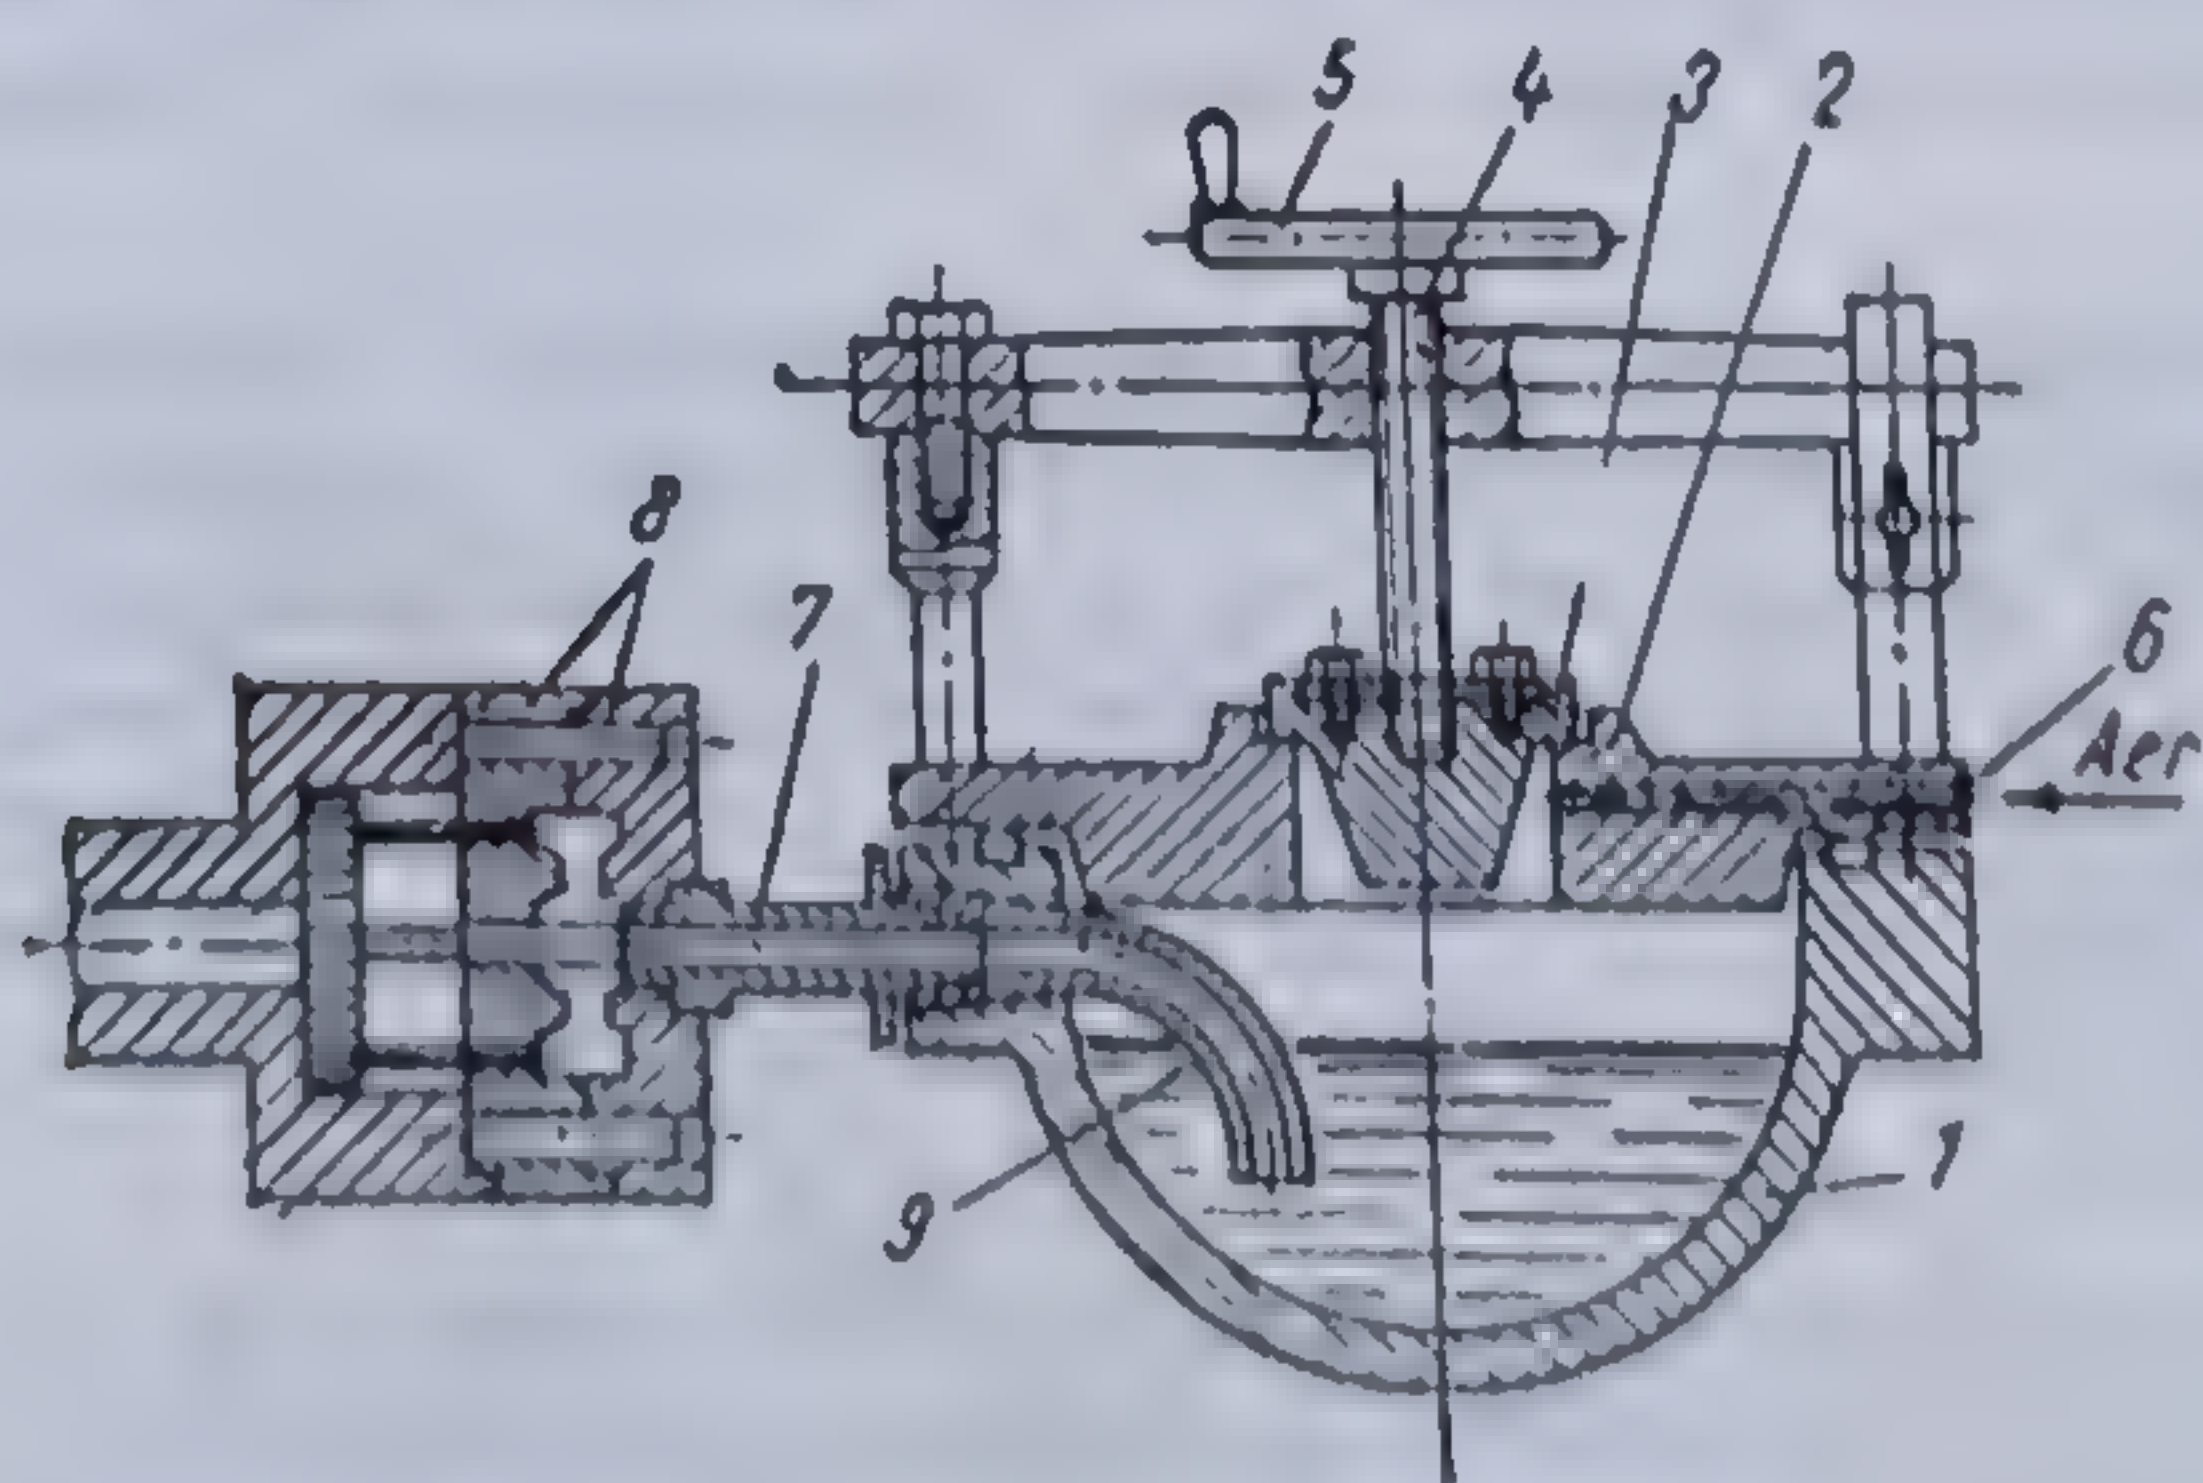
Schema mașinii de turnare sub presiune cu cameră caldă, cu compresor și ajutor.
